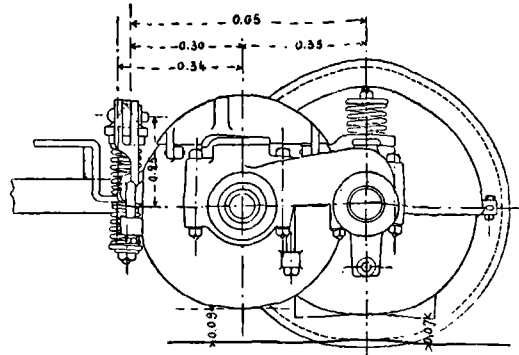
bis. — Moteur Walker n° 20. — Elévation longitudinale et plan. — Echelle 1/20.
